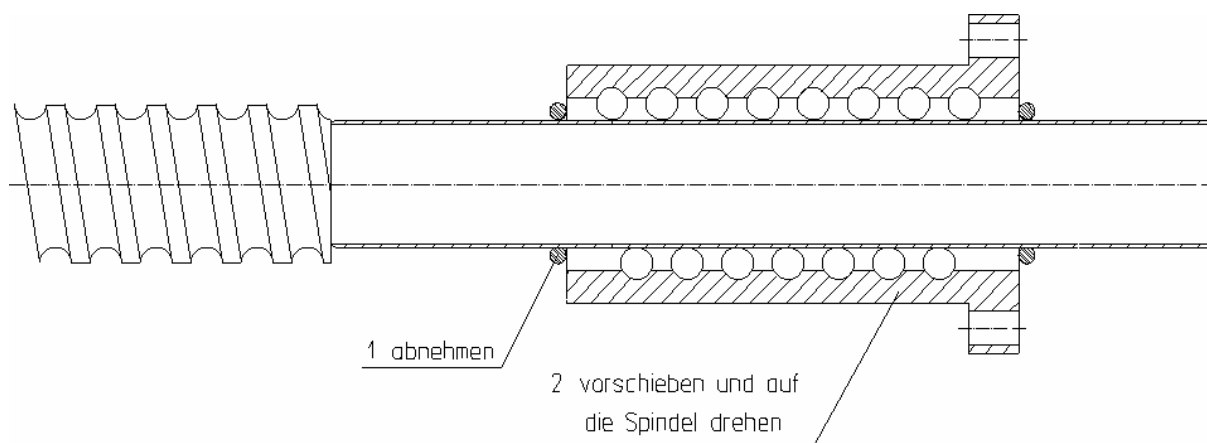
Demontage und Montage der Kugelgewindemutter
